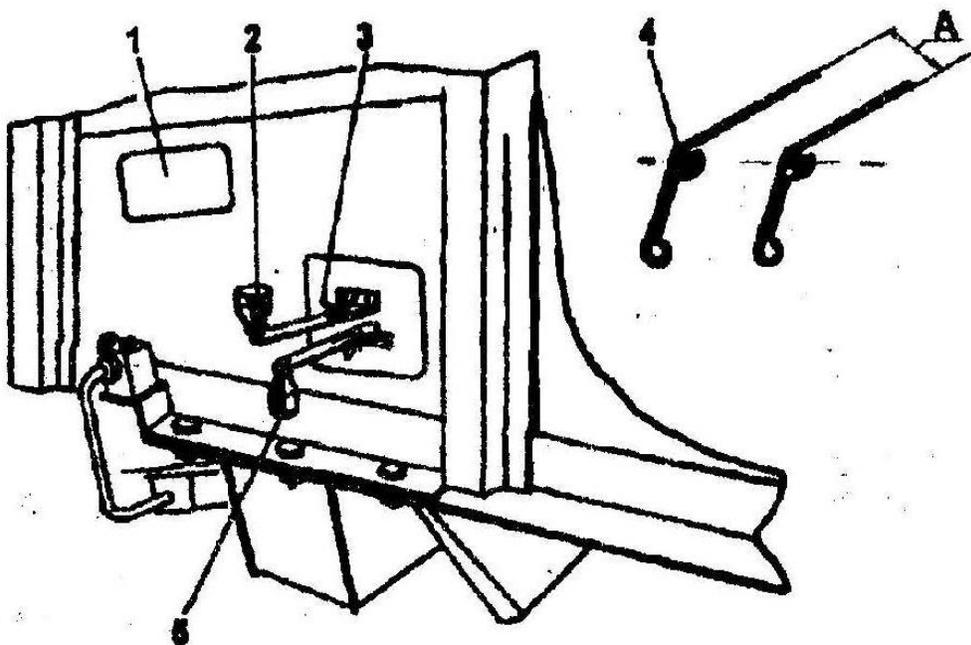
Механизм регулировки зазоров между жалюзи решета;
